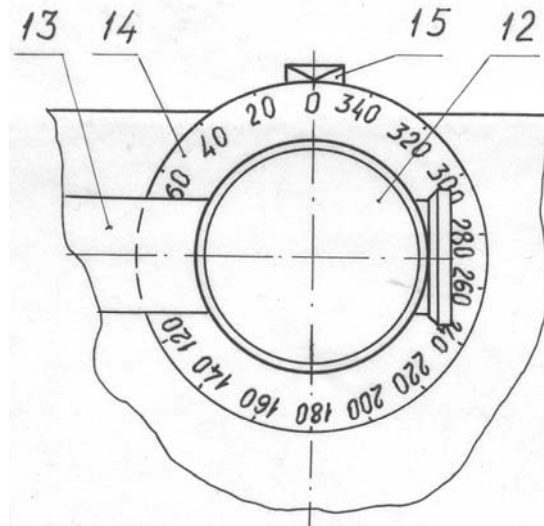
Вид по стрелке А (см. рис. 1)
